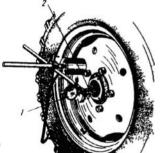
Измерение зазора в полшипниках переднего колеса.
